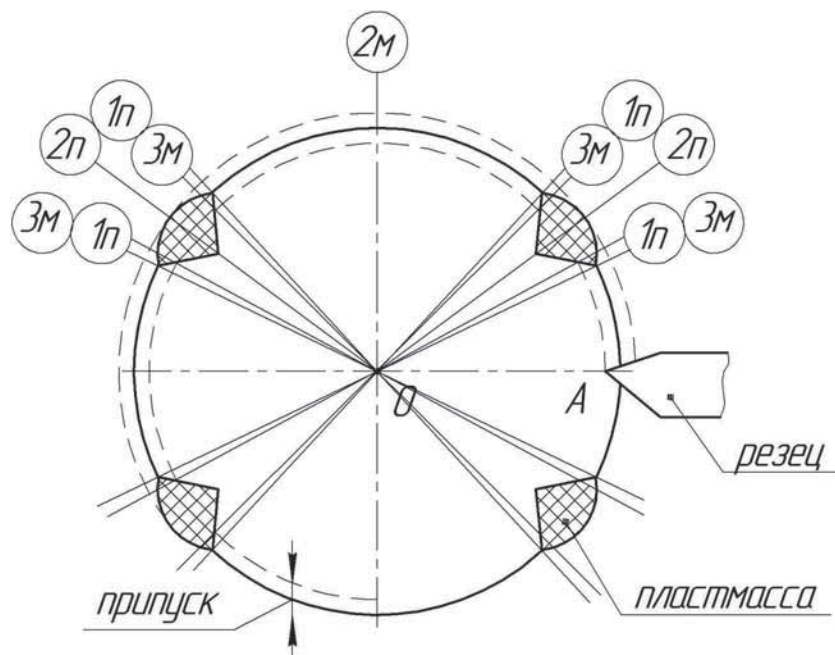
Схема обработки поверхности из двух конструктивных материалов (п – пластмасса, м – металл)
